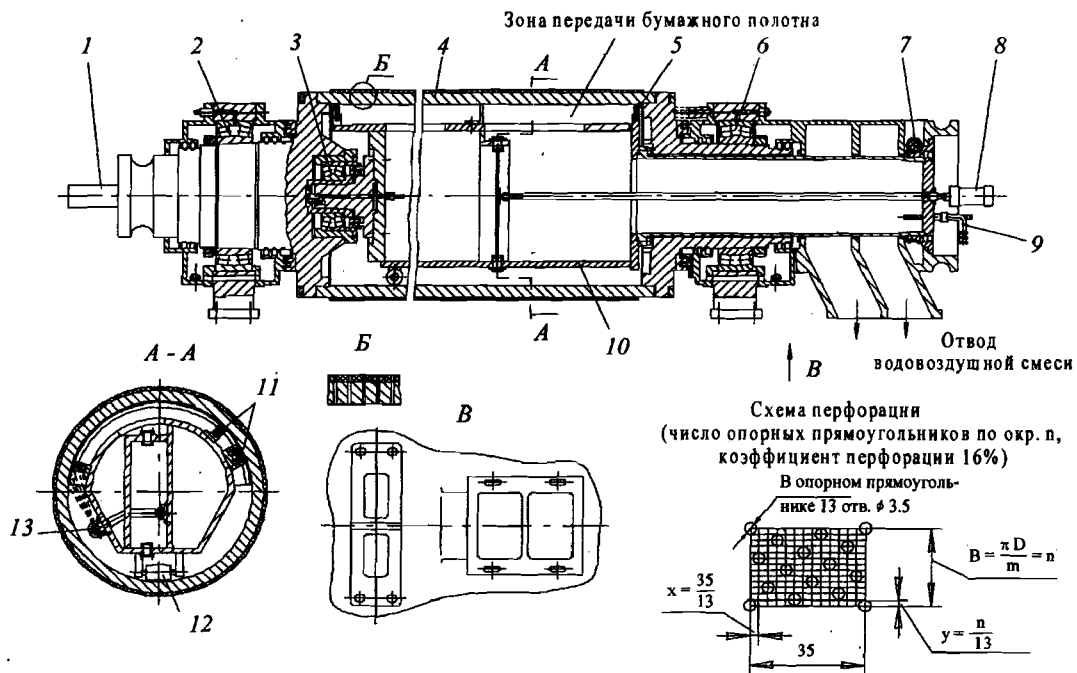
Отсасывающий вал: 1 - цапфа приводная; 2, 6 - подшипники вала; 3 - подшипник кмеры; 4 - рубашка (цилиндр) вала; 5 - уплотнение поперечное; 7 - червячная передача для поворота камеры; 8 - пневмоцилиндр заправочной зоны; 9 - труба для sprыска; 10 - камера; 11 - уплотнение продольное; 12 - ролик для выката камеры; 13 - sprыск
